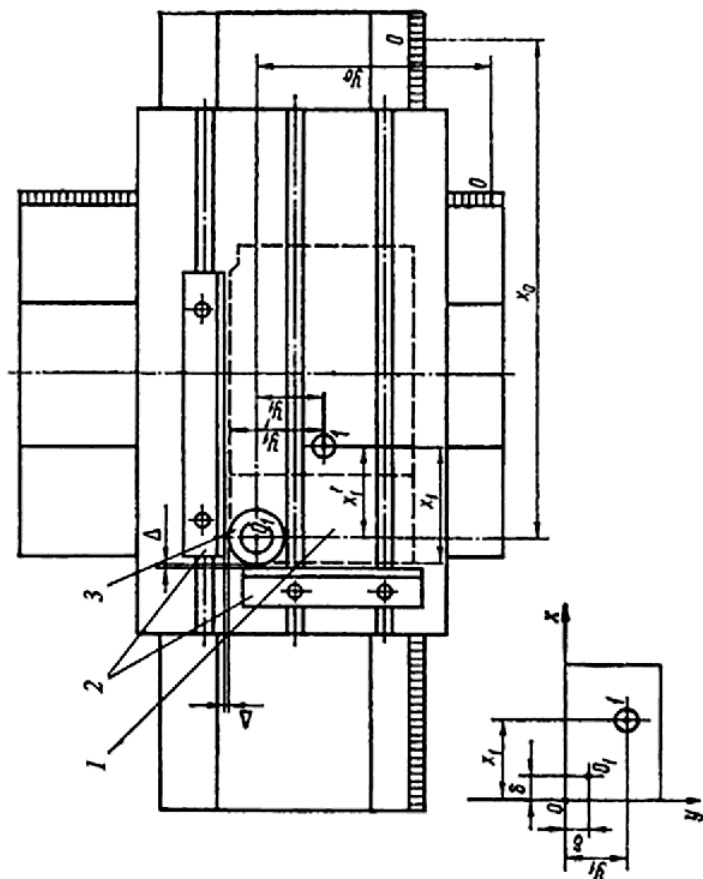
Схема установки стола сверлильного станка в исходное положение
